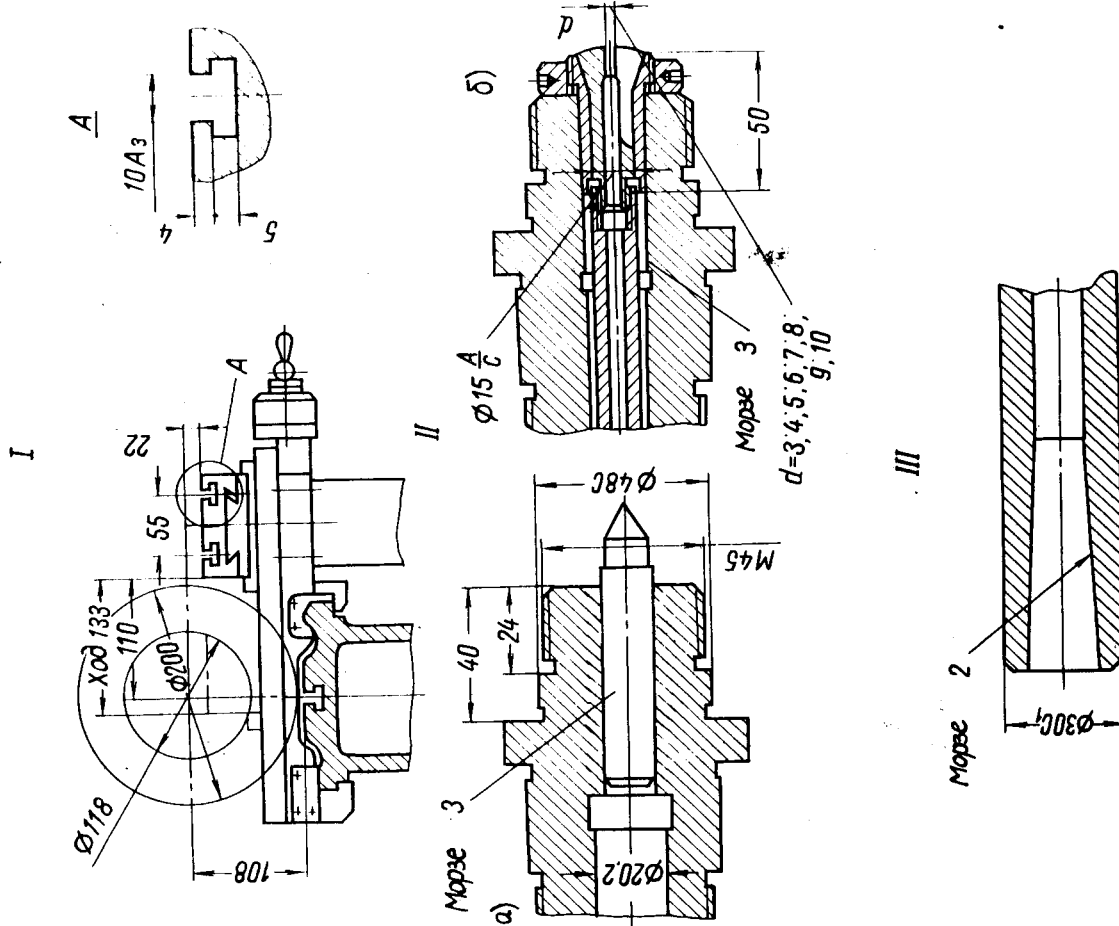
Габариты рабочего пространства. Посадочные и присоединительные размеры станка модели 16У04П:
